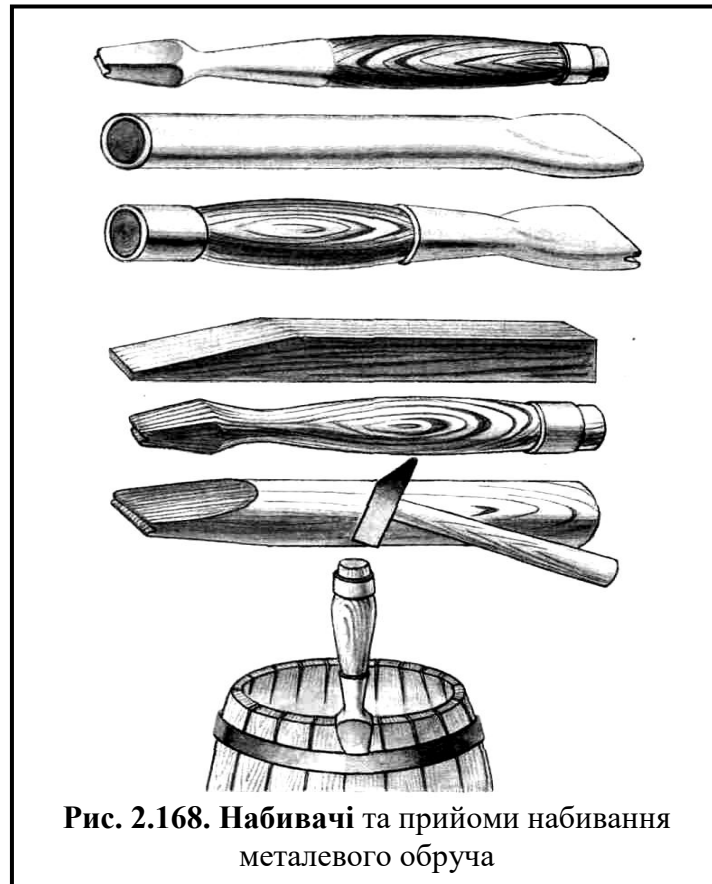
Набивачі та прийоми набивання металевго обруча
